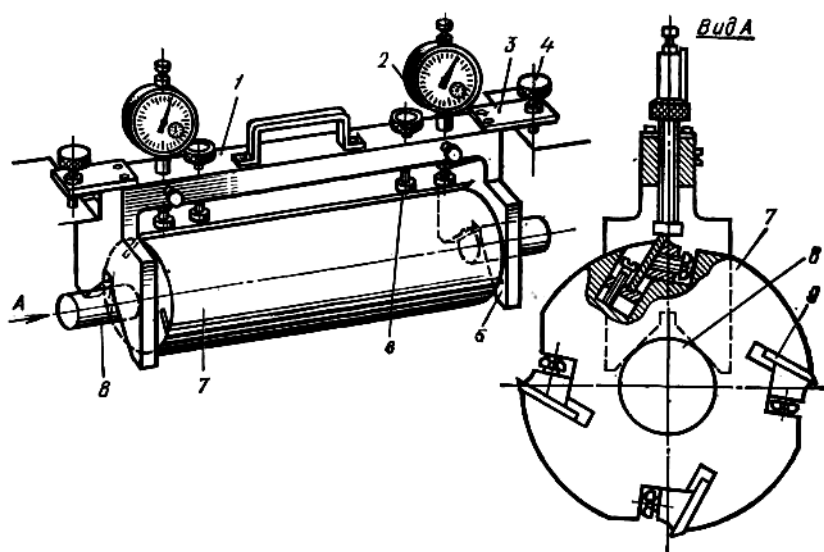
Контрольно-установочное приспособление с базированием на подшипниковых шейках ножевого вала: 1 — скоба, 2 — индикатор, 3 — пластинчатая пружина, 4 — винт крепления приспособления, 5 — базирующие элементы, 6 — упор, 7 — ножевой вал, 8 — шейка ножевого вала, 9 — нож
